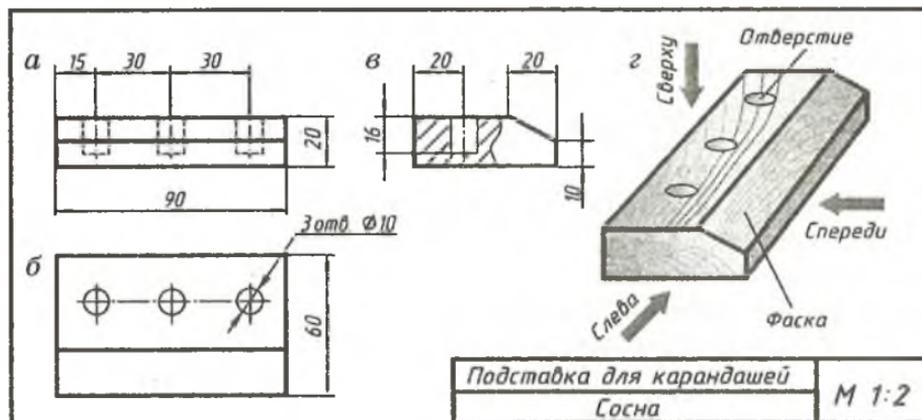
Чертеж подставки для карандашей: а — вид спереди; б — вид сверху; в — вид слева; г — технический рисунок
